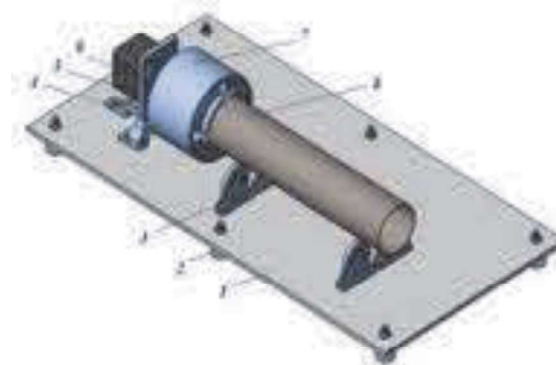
Узел вращения заготовки: 1 – основание; 2 – регулируемые опоры; 3 – роликовые опоры; 4 – держатель для привода; 5 – привод; 6 – узел подшипниковый; 7 – цанговый зажим; 8 – заготовка
